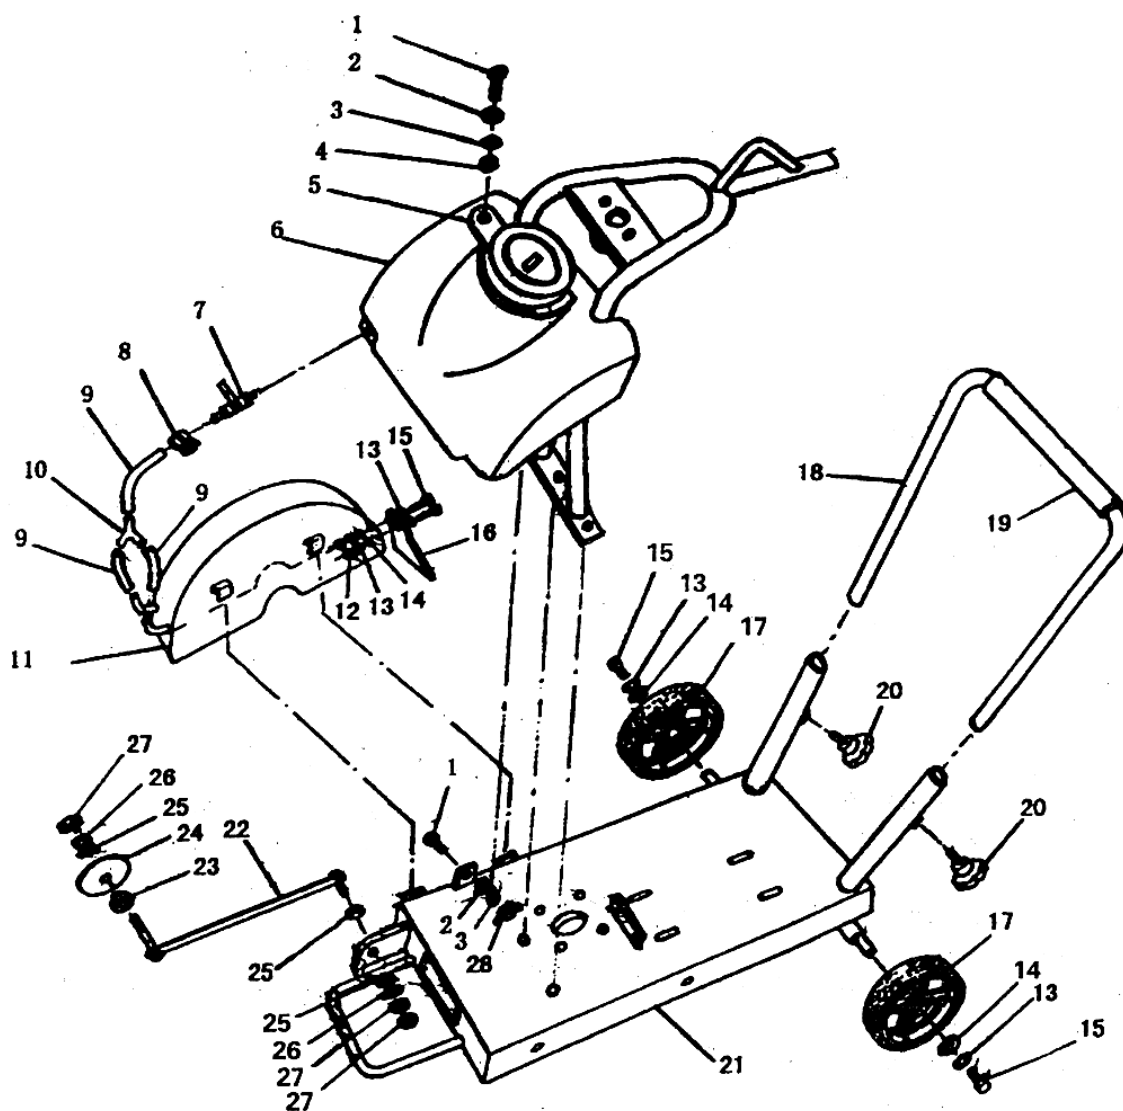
Ensemble châssis, réservoir d'eau et carter de disque
